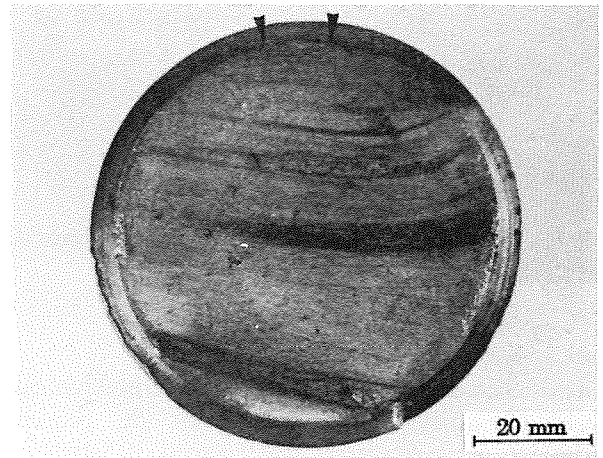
Aspecto de la superficie de fractura del lado de la parte roscada del tirante. Las flechas indican el inicio de la fractura.
